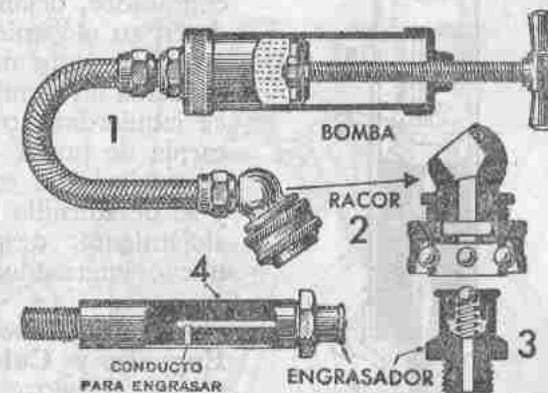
Bomba 1, racor 2 y engrasador 3 para el engrase a presión del chasis.
